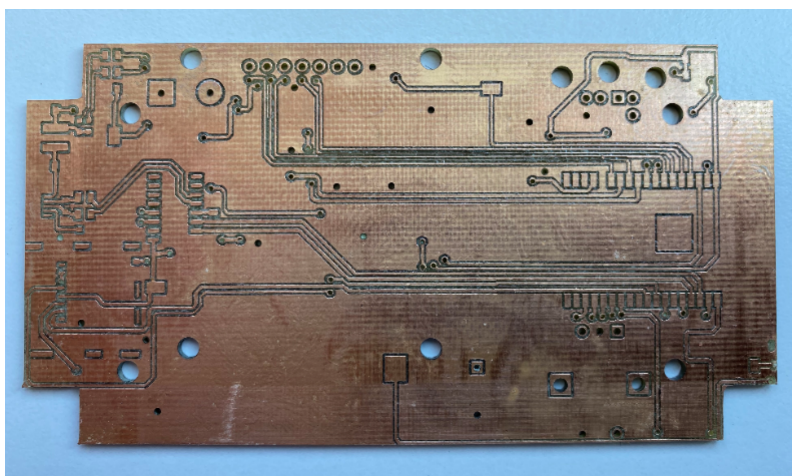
Vista superior PCB fabricada en GranaSAT
